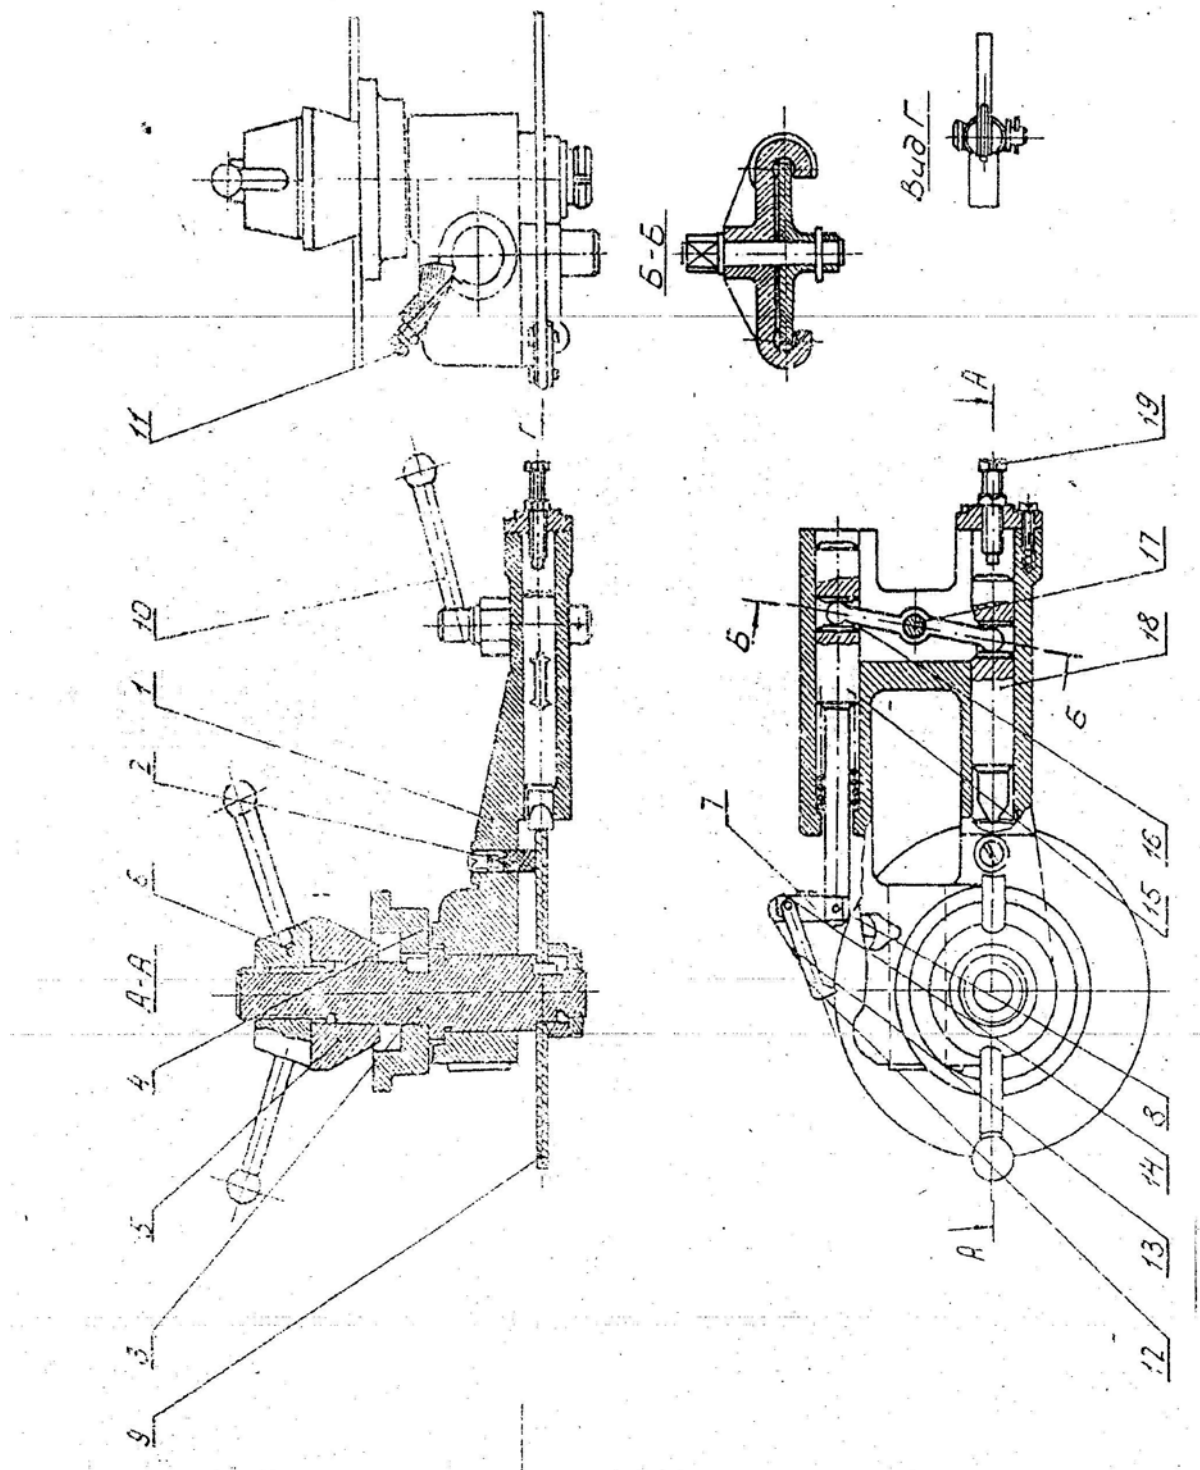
Приспособление для насечки и обрезки зубьев круглых пил
